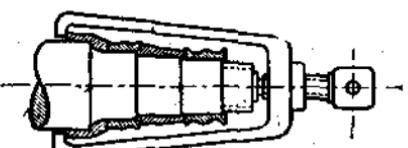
Приспособление для снятия внутреннего кольца элемента шарикоподшипника.
